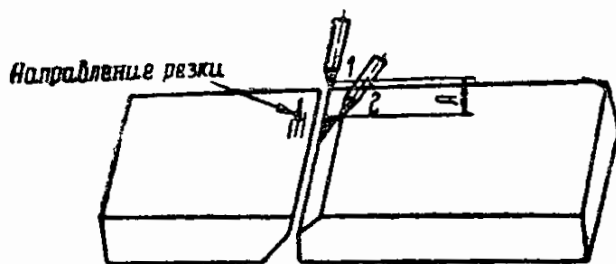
Кислородная резка деталей из листовой стали одновременно двумя резаками.
